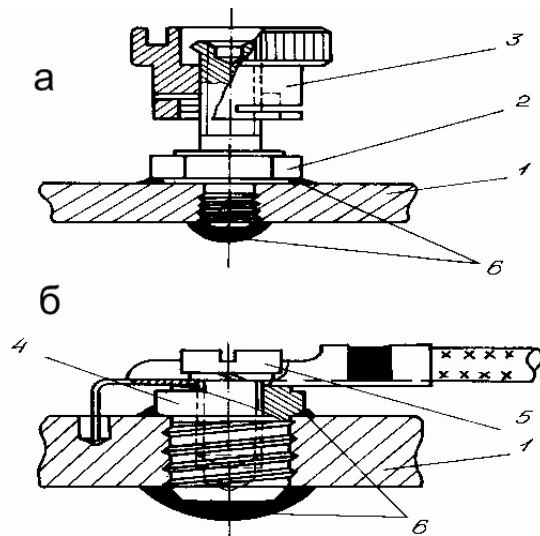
Рознімні затискачі заземлення: а – легко розбірний затискач; б – затискач під викрутку; 1 – корпус; 2 – гвинт-затискач у тілі корпусу; 3 – гайка-затискач; 4 – гніздо-затискач у тілі корпусу; 5 – гвинт-затискач; 6 – компаунд ЕЗК 6
